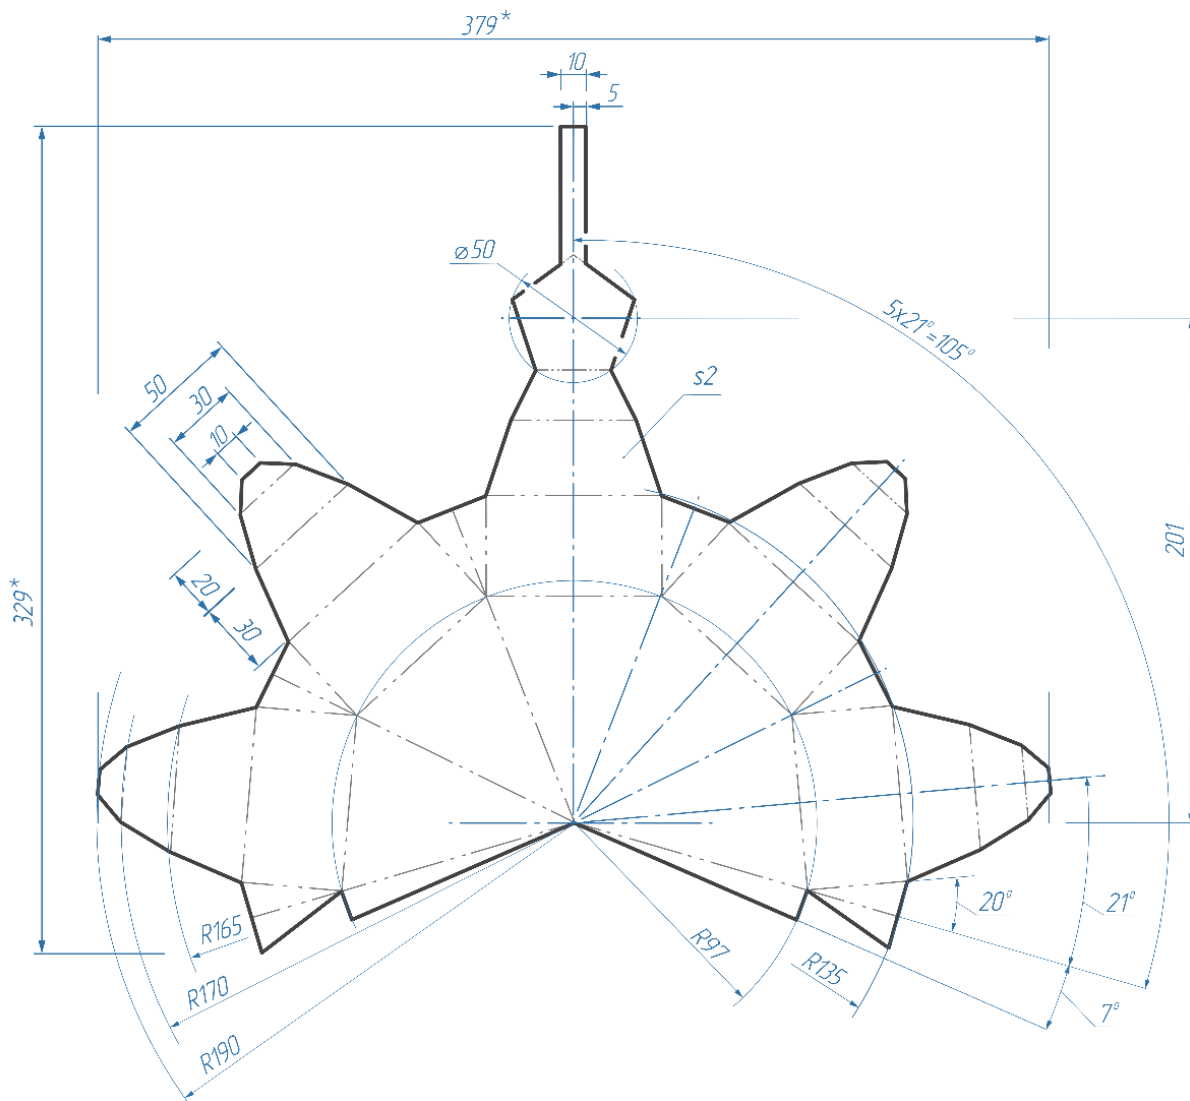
Обозначение размеров между равномерно расположенными одинаковыми элементами объекта на развертке упаковки для кондитерских изделий
